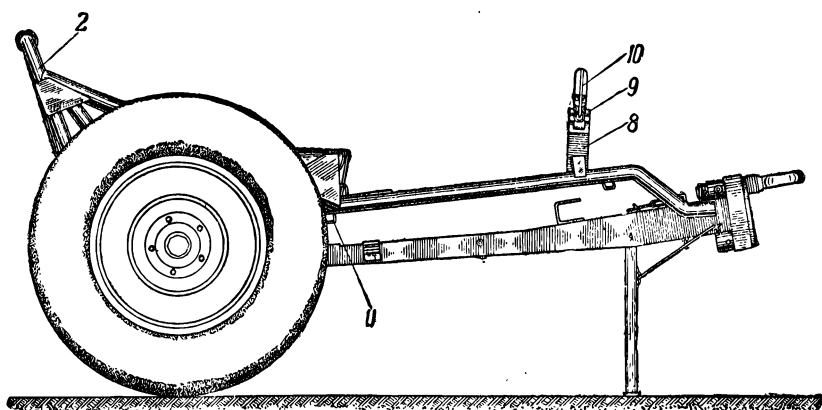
Колёсный ход конструкции завода № 702. Общий вид (без ящика для ЗИП):
